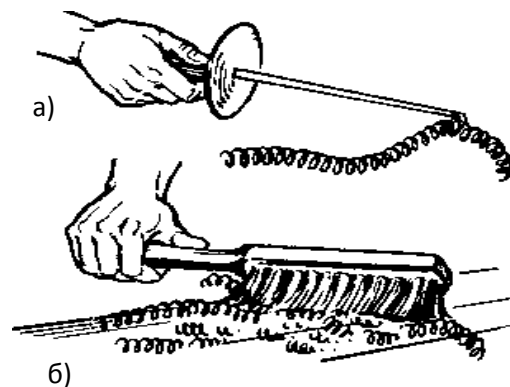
Видалення стружки з верстата за допомогою: а - гачка; б - щітки
